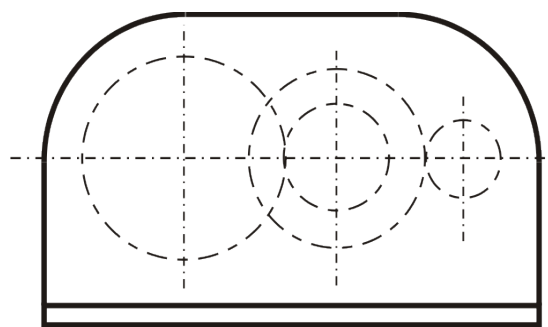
Кинематическая схема двухступенчатого горизонтального редуктора с раздвоенной первой (быстроходной) ступенью
